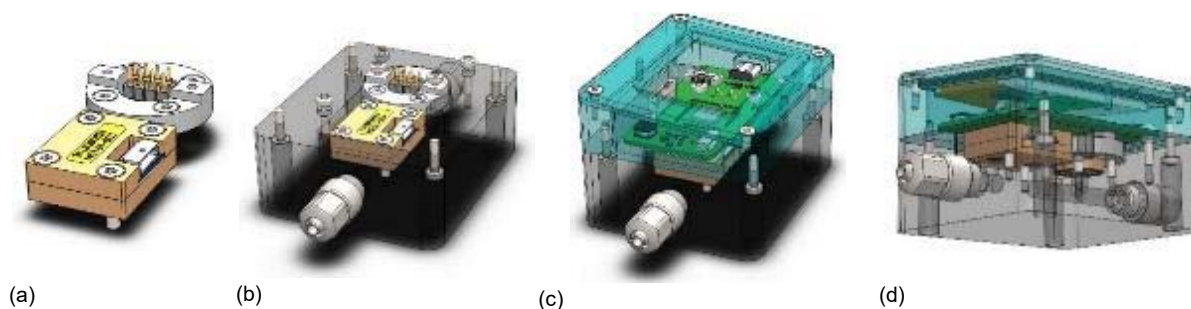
Transparente 3D CAD *Solidworks* Ansichten der Module (a), die in den Grundkörper eingebaut sind (b), mit aufgesetztem Deckel (c) und Fluidzuführung (d).
